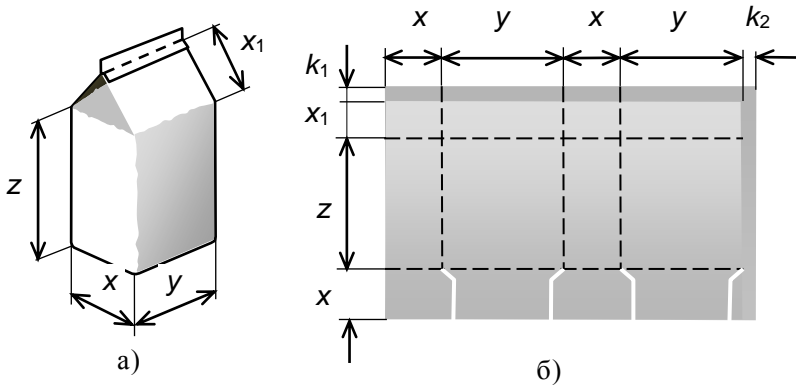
Паперовий пакет для пакування сипкої продукції: зовнішній вигляд та геометричні параметри (а); схема розгортки (б)
